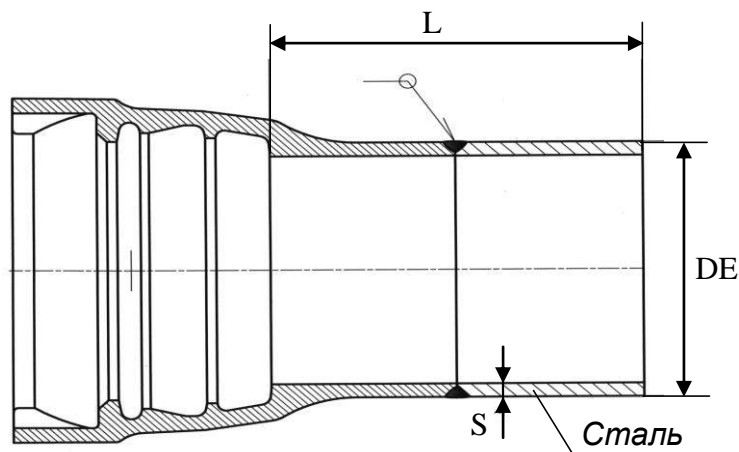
Патрубок фланец – раструб (расположение сварного шва зависит от вида фланца)
